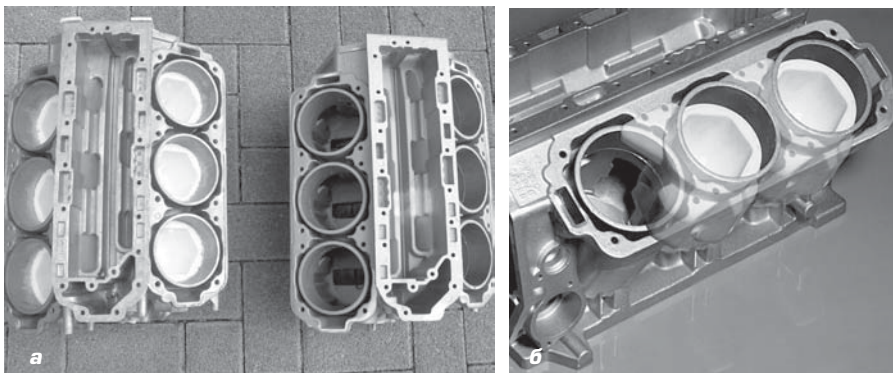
, а, б. Блоки цилиндров, изготовленные литьем под дав-
